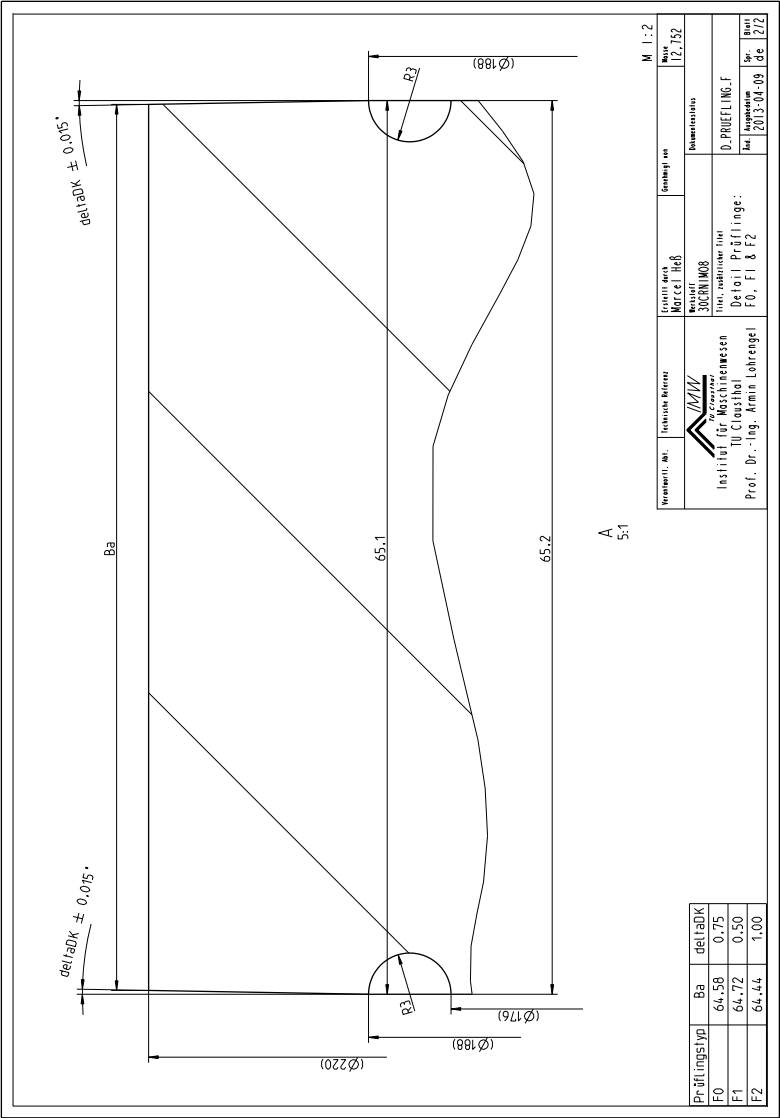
Detailzeichnung für Prüflinge des Typs F: Prüflingsgeometrie mit ebenen Laufflächen.
